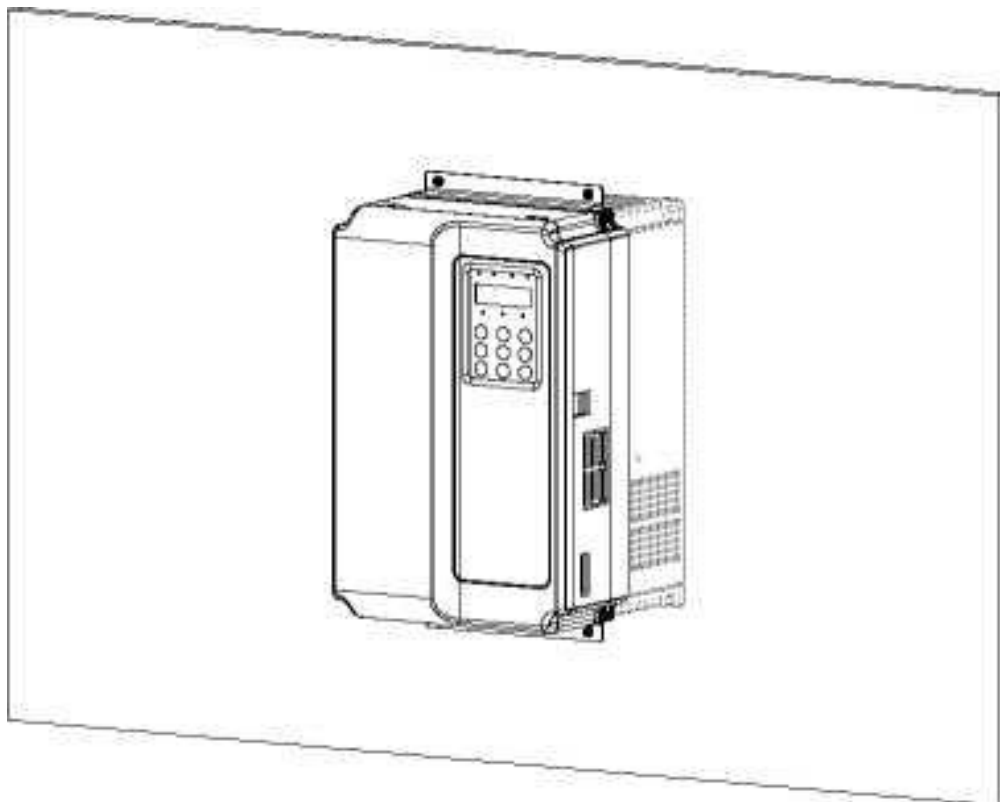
Сквозной монтаж устройства INVERTER (пластиковый корпус)
